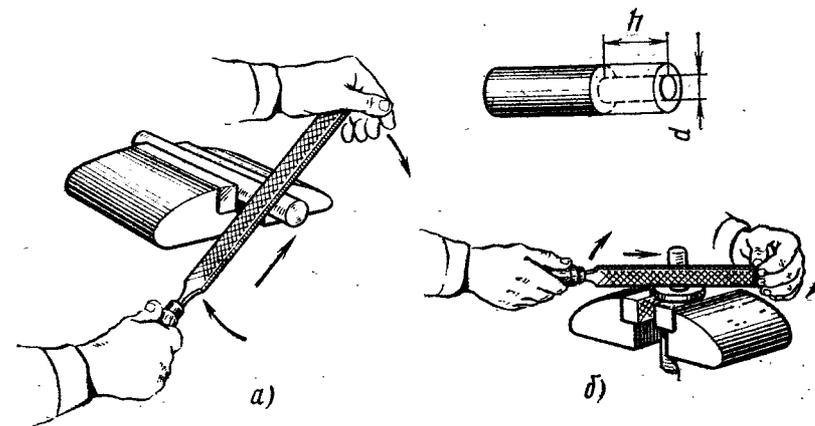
Заготовка и приемы опиливания цилиндрической поверхности с установкой заготовки в тисках: а — горизонтально; б — вертикально
